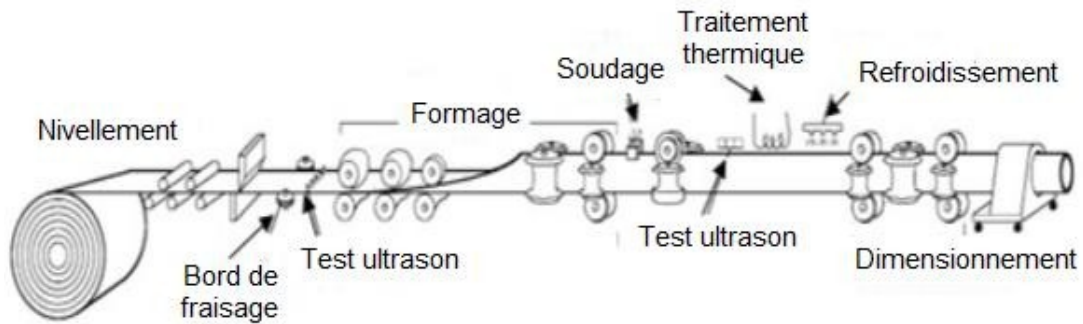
Technique de fabrication des tubes soudés en spirale [7].
